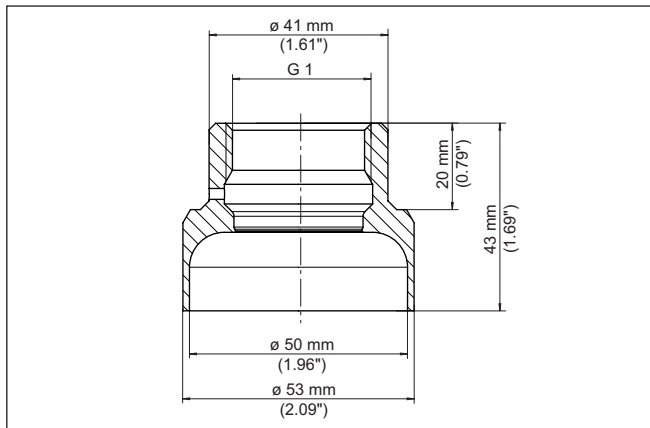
Dimensiones racor para soldar directo para montaje en tubería G1 (ISO 228-1) - Junta tórica
